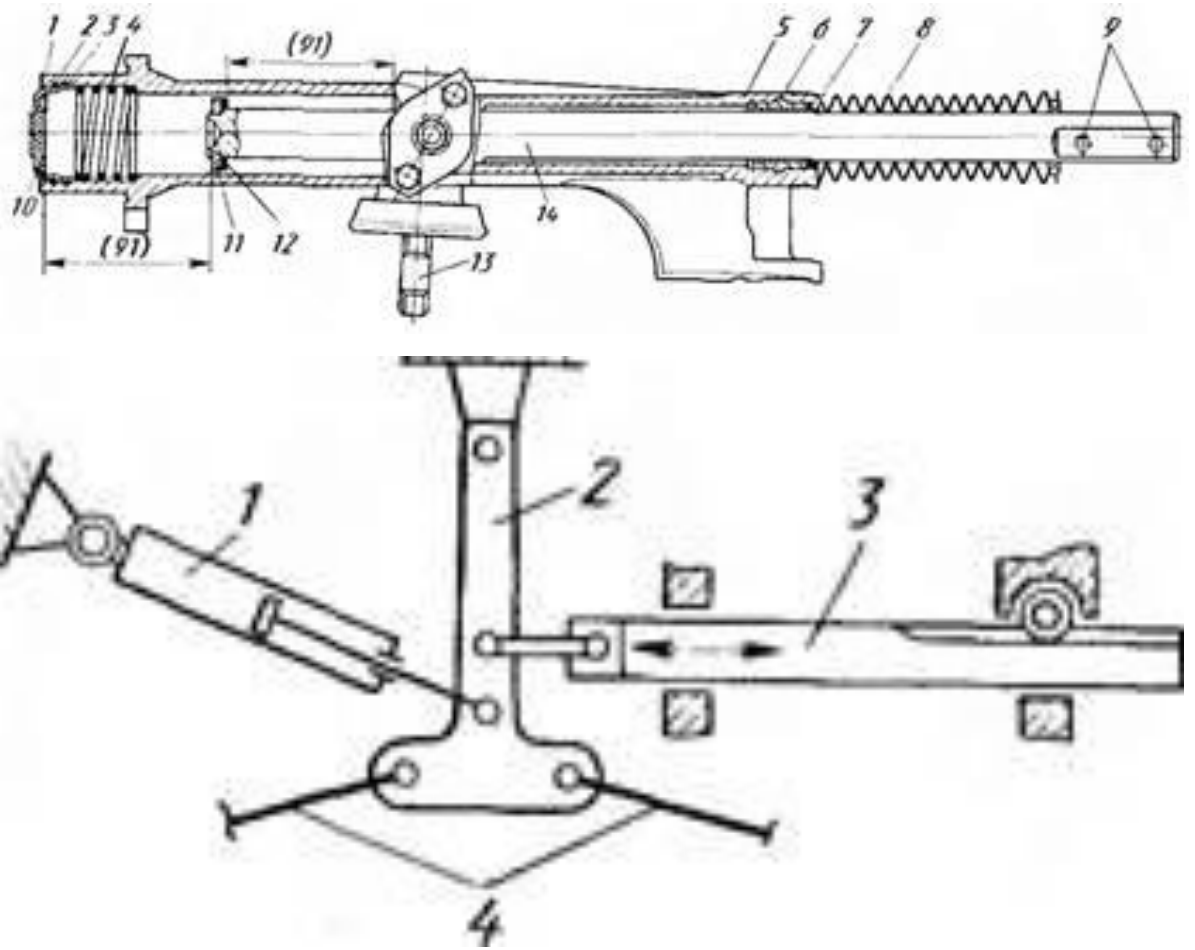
Боковое расположение шестерни при креплении боковых тяг к середине зубчатой рейки
